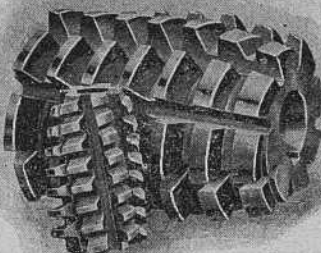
Fresa de visinfín para engranajes rectos y helicoidales.
